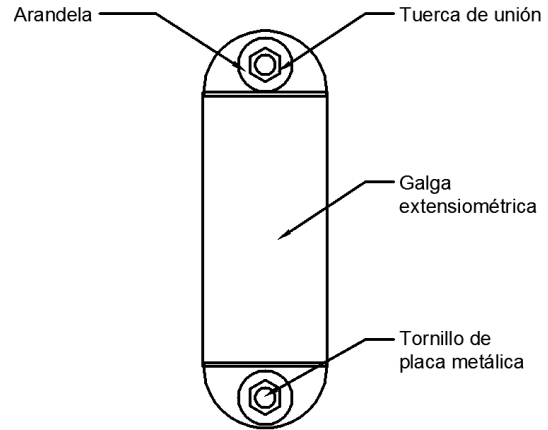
Vista en planta de la unión viga-galga extensiométrica
